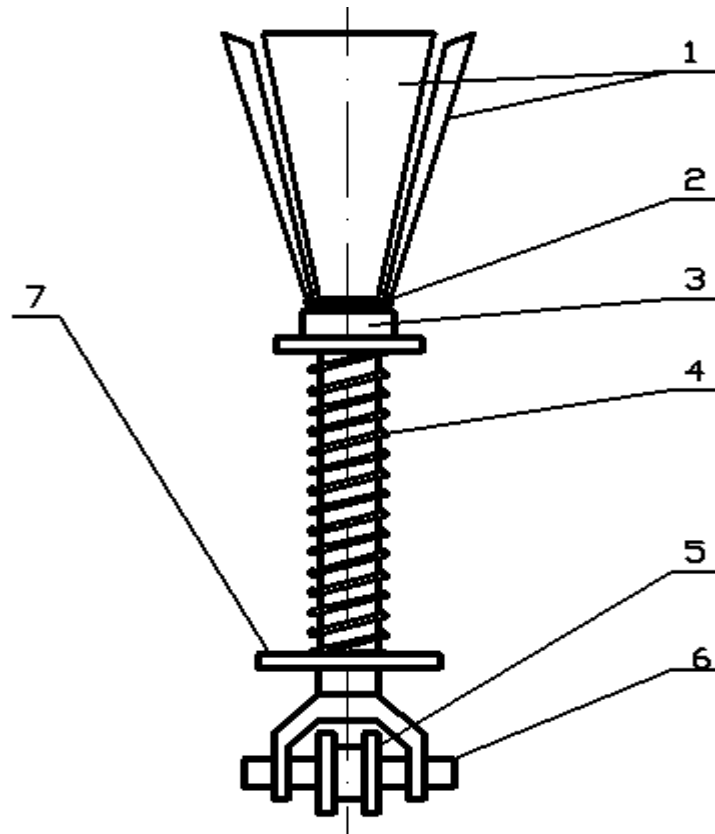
Плодоутримувач: 1 – стулки; 2 – шарнір; 3 – шток; 4 – пружина;
